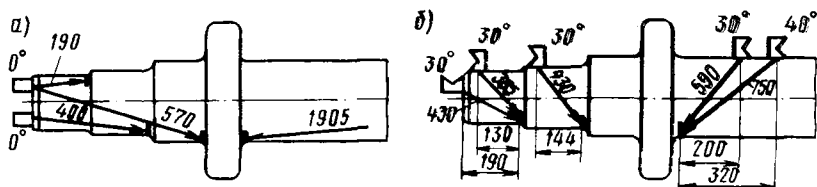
Схемы и зоны контроля прямым и наклонным искателями со стороны торца главного приводного вала эскалатора Н-40 очереди III и IV.
